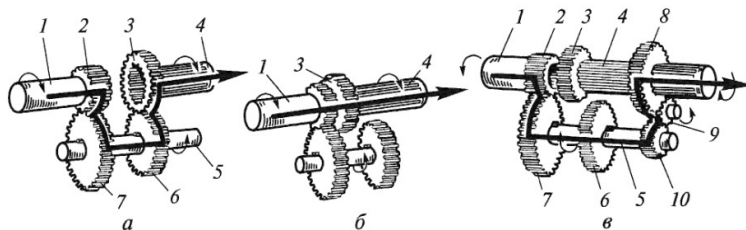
Схема работы трехвальной коробки передач: *а* — схема включения передач через шестерни 2, 3, 6, 7, промежуточный вал 5 на вторичный вал 4; *б* — прямая передача с первичного вала 1 на вторичный вал 4 через шестерню 3; *в* — схема включения заднего хода
